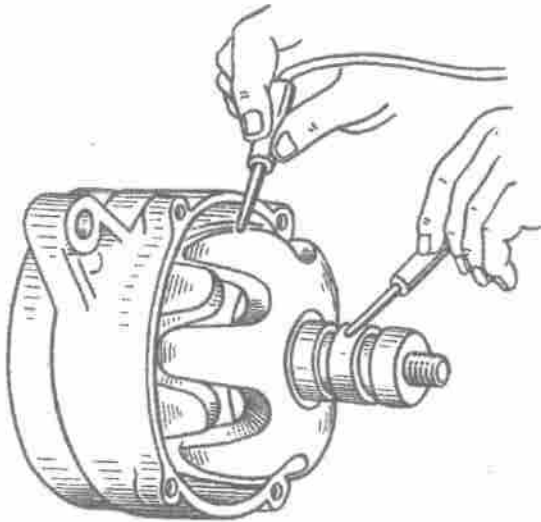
Prüfen der Läuferwicklungen (auf Gehäuse-schluß)
